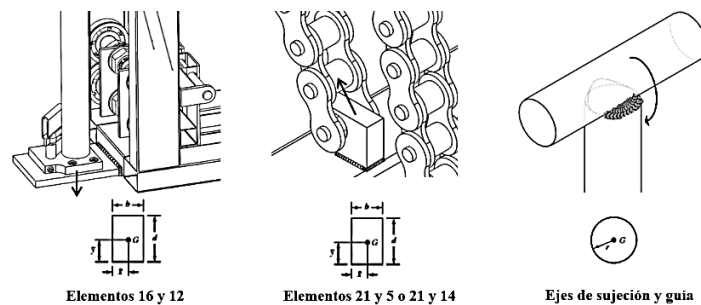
Soldaduras en elementos del sistema de elevación.
